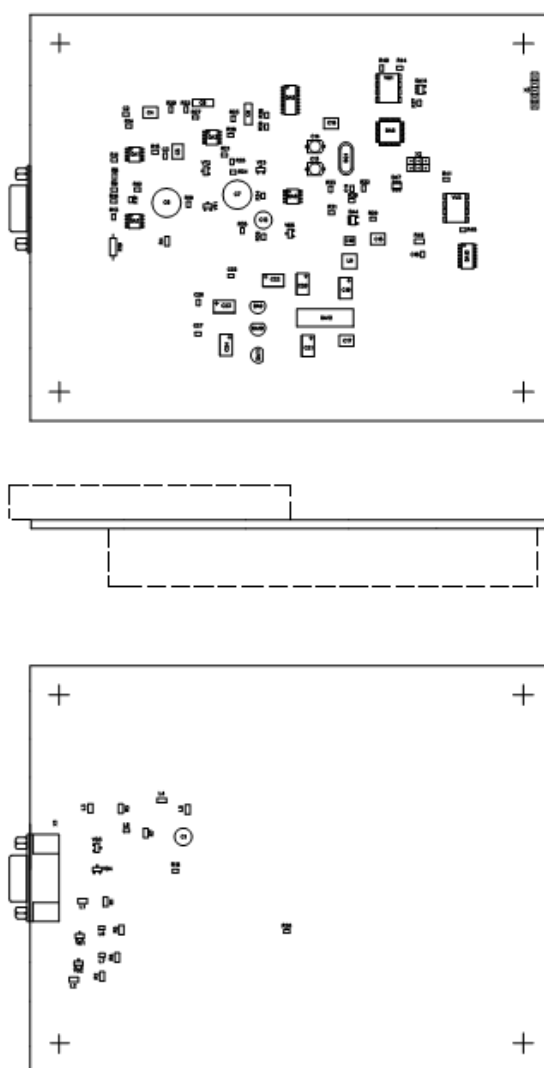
Сборочный чертеж модуля ЭЭГ
